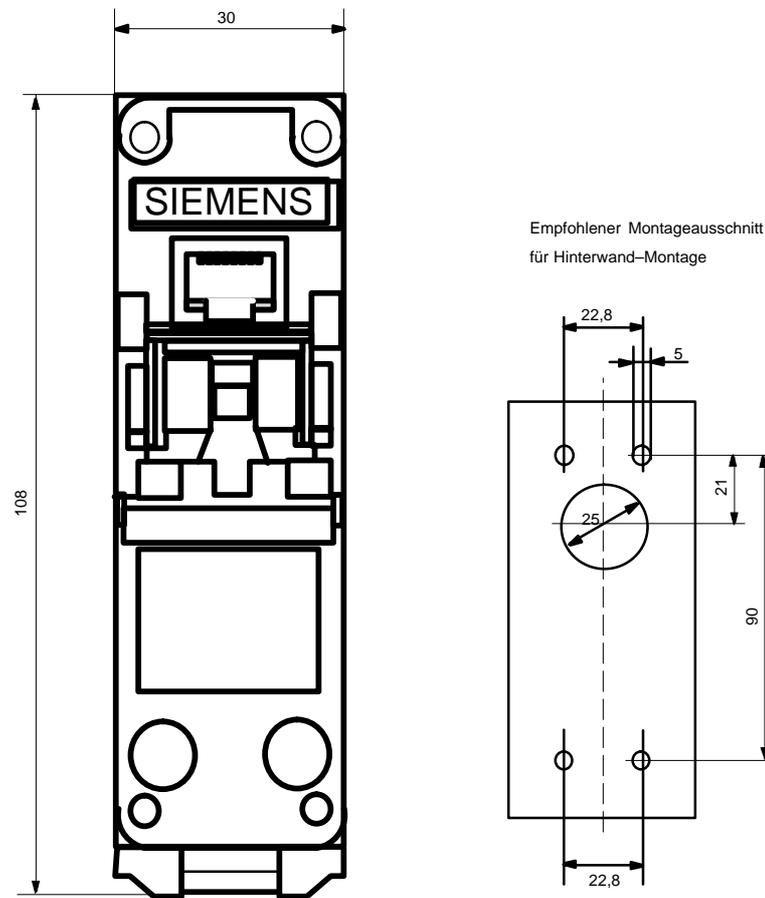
IE FC Outlet RJ45 (Maße in mm)
